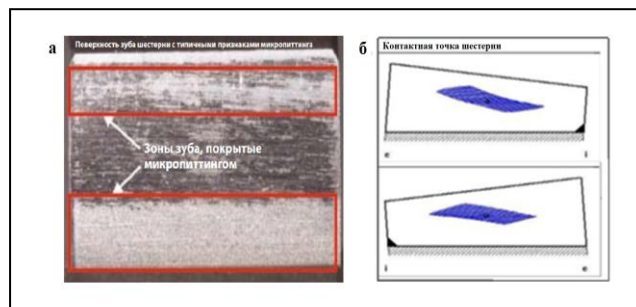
Макропиттинг (а) и микропиттинг контактных поверхностей зубчатых колес (б)
